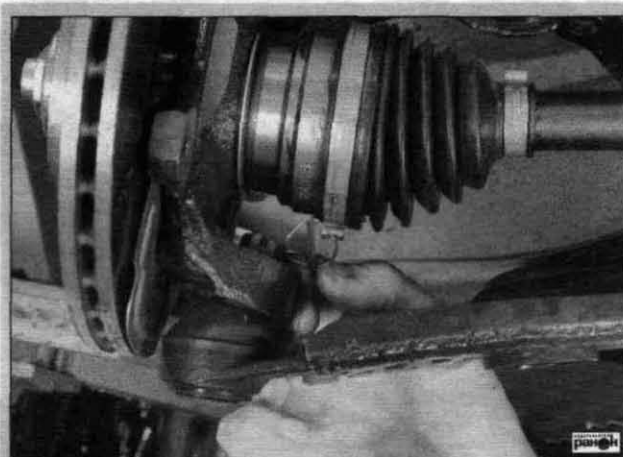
Извлечение дужки фиксатора гайки крепления шаровой опоры
